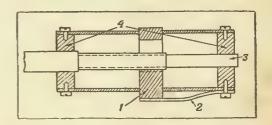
Супорт т. Трушина: 1—полугайка; 2—пружина, сцепляющая полугайку с резьбой винта; 3— напранляющая с инетои; 4— напранляющие втулки
